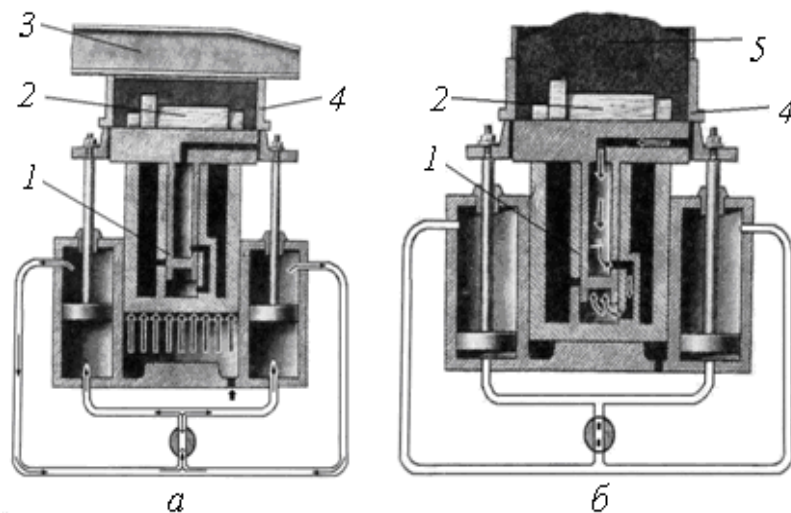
Схема пневматичної струшувальної машини: а – ущільнення формової суміші з підпресуванням; б – ущільнення без підпресування; 1 – робочий циліндр; 2 – модель; 3 – траверса; 4 – опока; 5 - формова суміш
